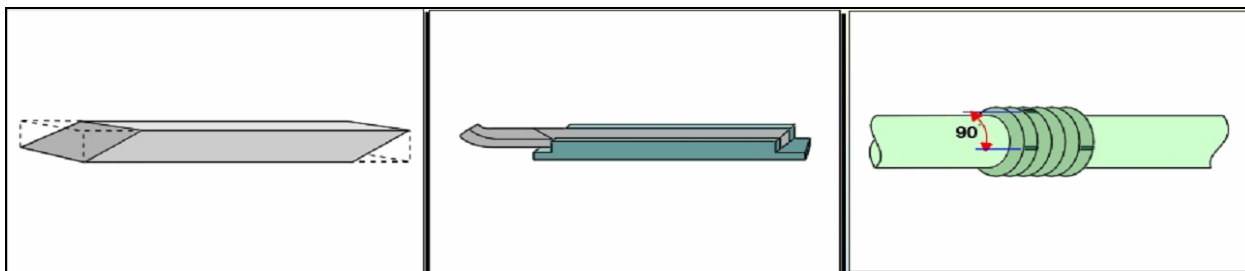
Corte oblíquo, dispositivo de corte e posicionamento das gaxetas.
